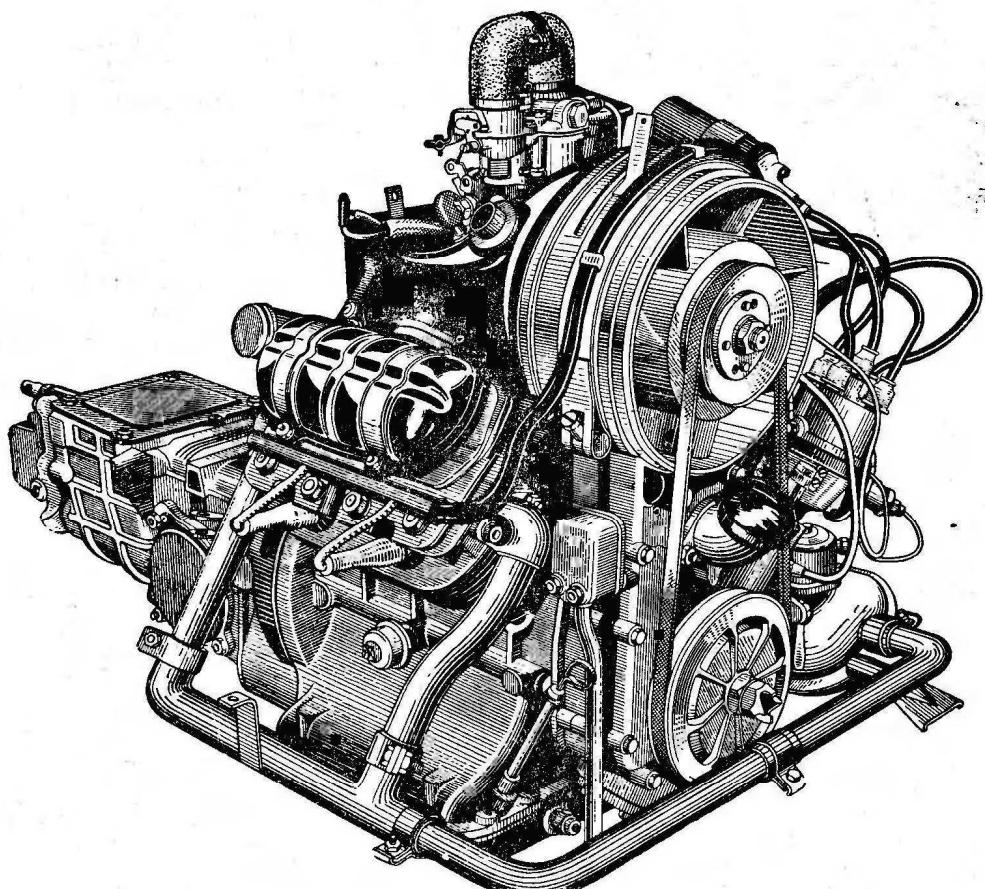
Motor mit Wechselgetriebe und Hinterachsantrieb
